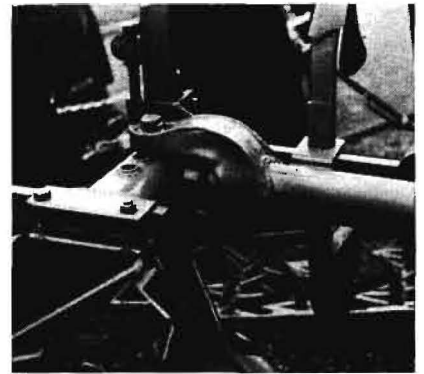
Gabelkopf eines Drehpfluges aus Blechteilen geschweißt. Verstellbar in Buchsen eines ovalen Querrohres. An die Stirnfläche dieses Querrohres ist ein Blechstück geschweißt, das die Klemmverbindung zu einem Flacheisen des Rahmens bildet
